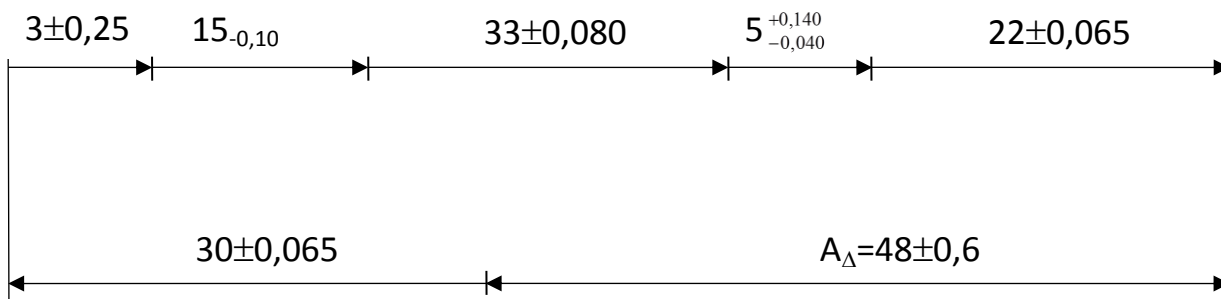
Схема размерной цепи (метод max – min)
